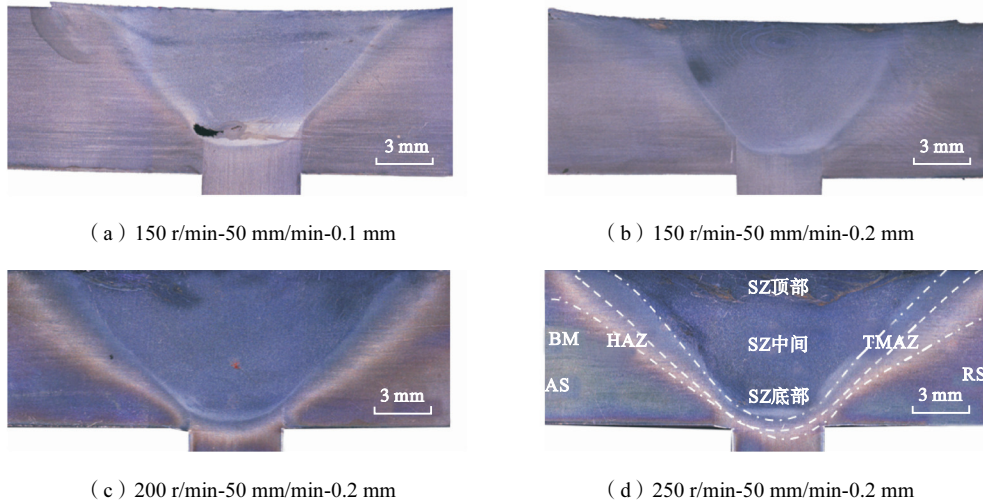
不同焊接参数下钛合金 T 形接头焊缝横截面
